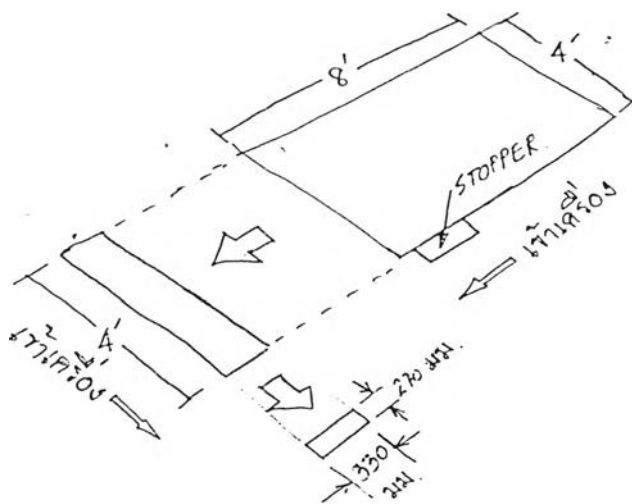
เครื่องตัดเหล็ก SHEAR MACHINE
